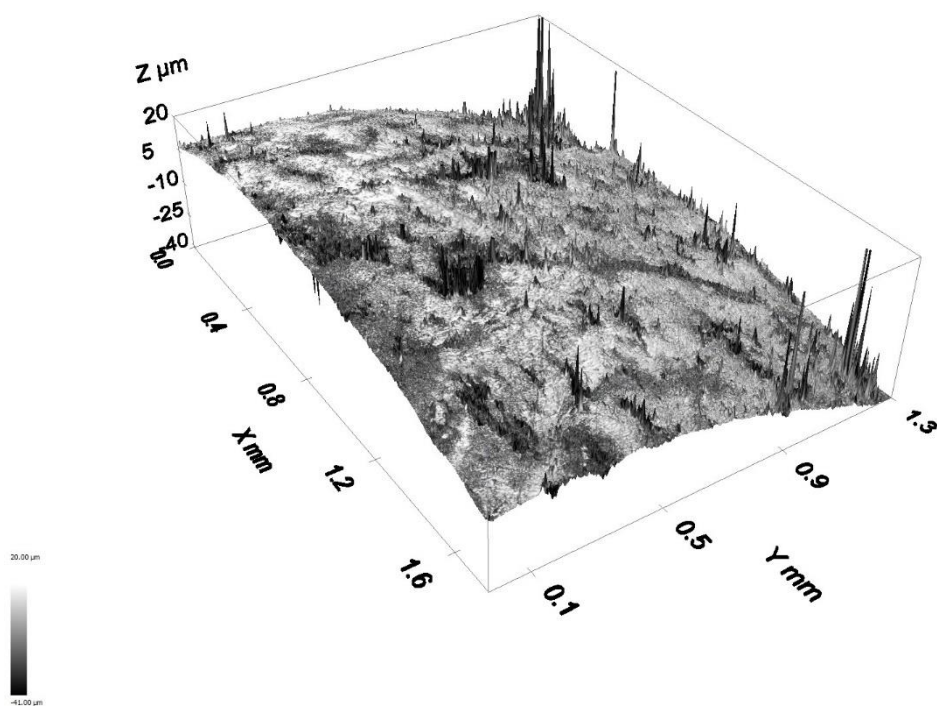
Imagem tridimensional da superfície da cabeça do perno-L.
